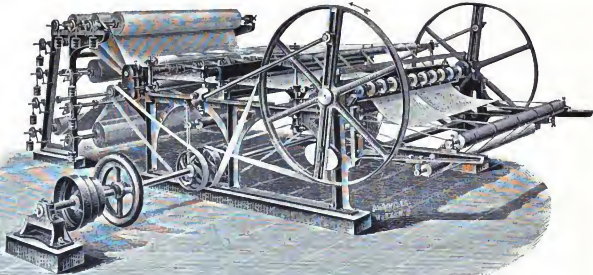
Papierschnidmaschine von der Maschinenbauanstalt Götzern.
